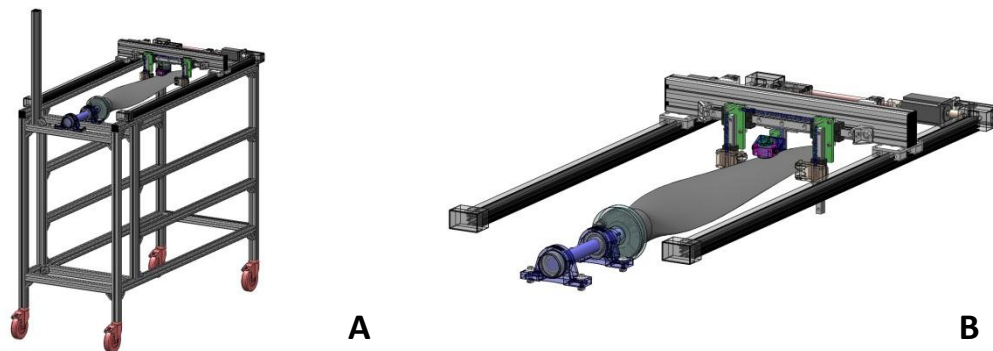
Modelação em SolidWorks do Protótipo #3: a) vista geral; b) vista de pormenor.
